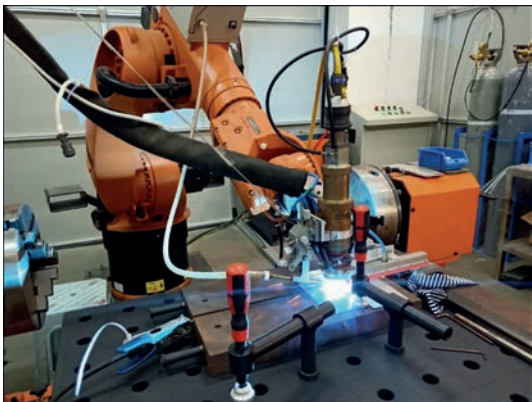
Зовнішній вигляд стенду для лазерно-плазмового зварювання із застосуванням робота KUKA KR30HA в процесі роботи
